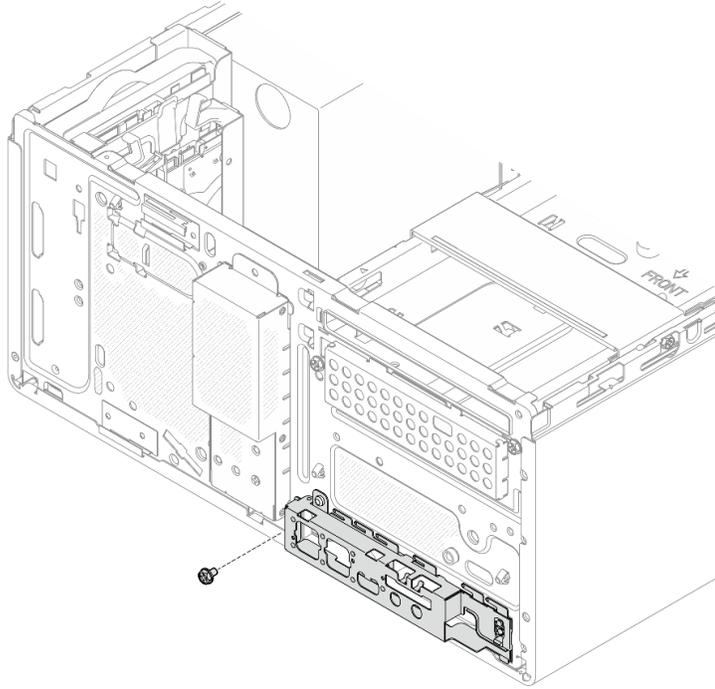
Extracción de los tornillos que fijan el marco biselado frontal al chasis
